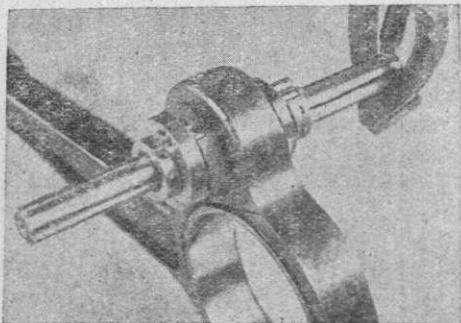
Приспособление для расшлифовки проушины главного шатуна мотора М-17.
